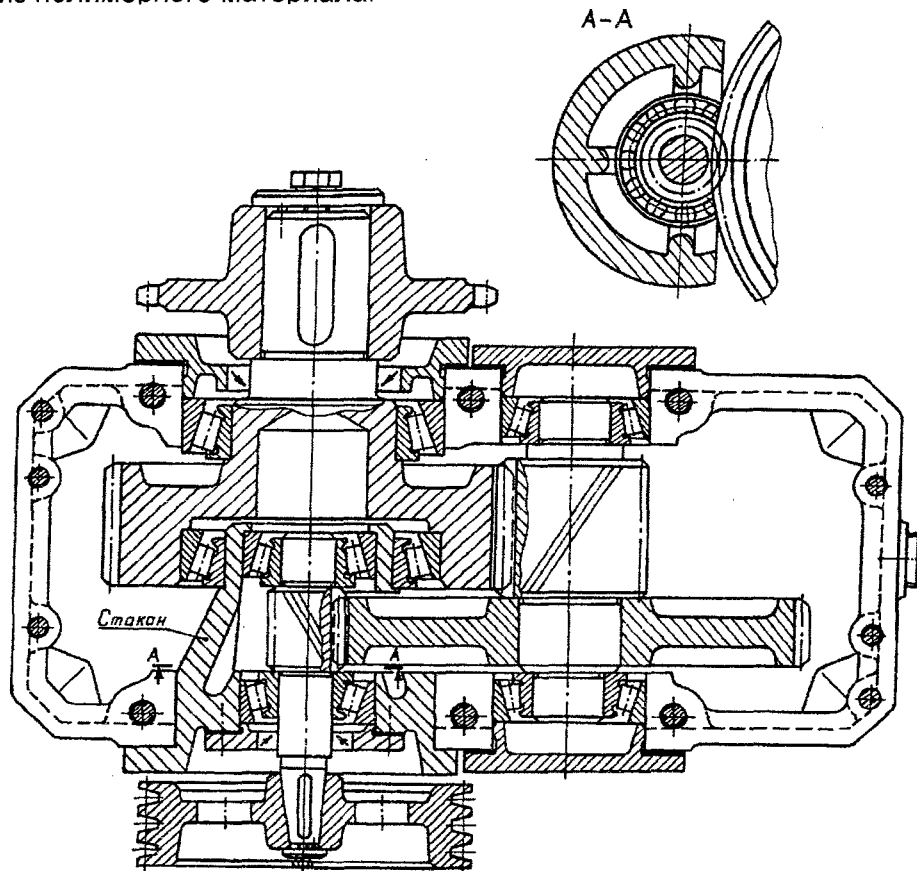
Двухступенчатый цилиндрический горизонтальный соосный редуктор без внутренней стенки в корпусе
